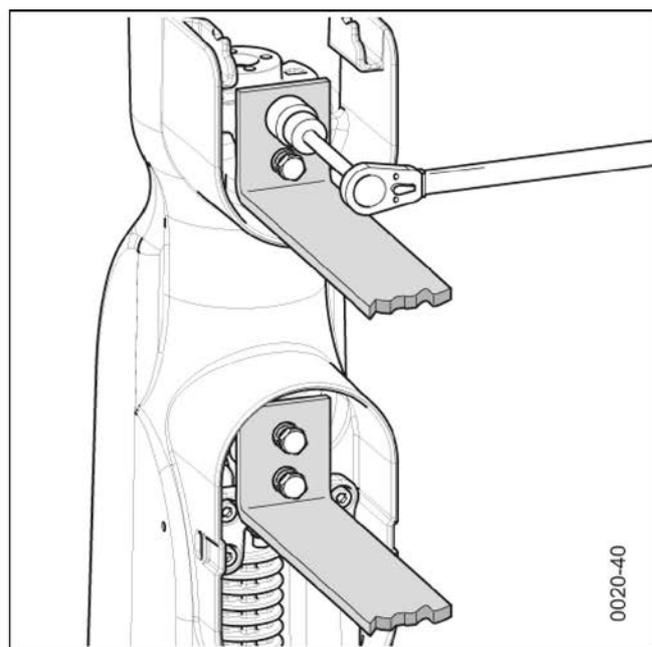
Установка шин (угловых). Пример для номинального тока 1250 А
